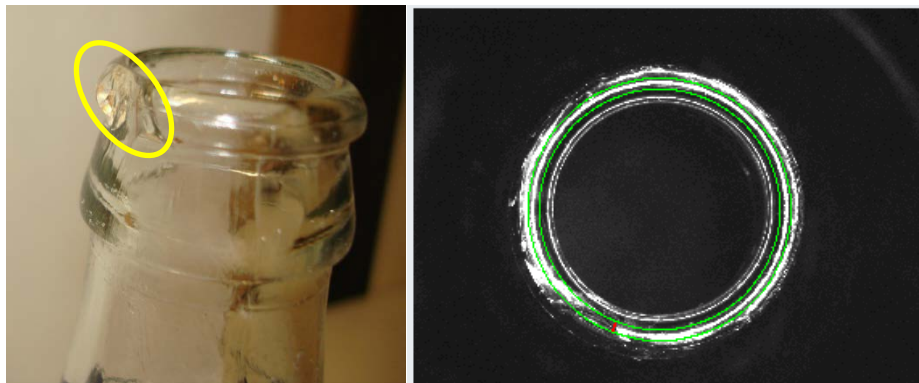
Defecto de botella (Izquierda) y vista a través del inspector (Derecha).
